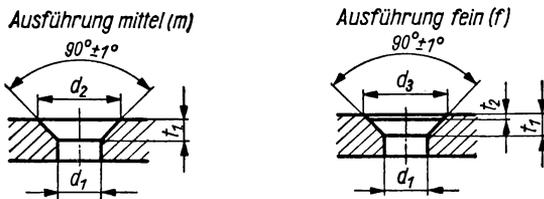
Senkungen nach TGL 0-75 für Senkschrauben
